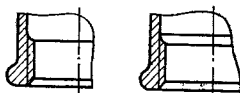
Варианты конструктивного исполнения деталей с внутренней резьбой
